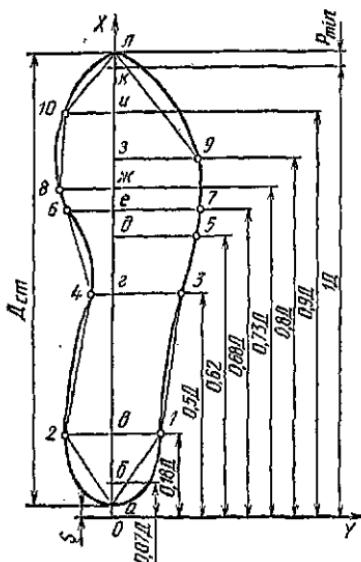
Схема расположения наколов для проверки обхватов колодки
